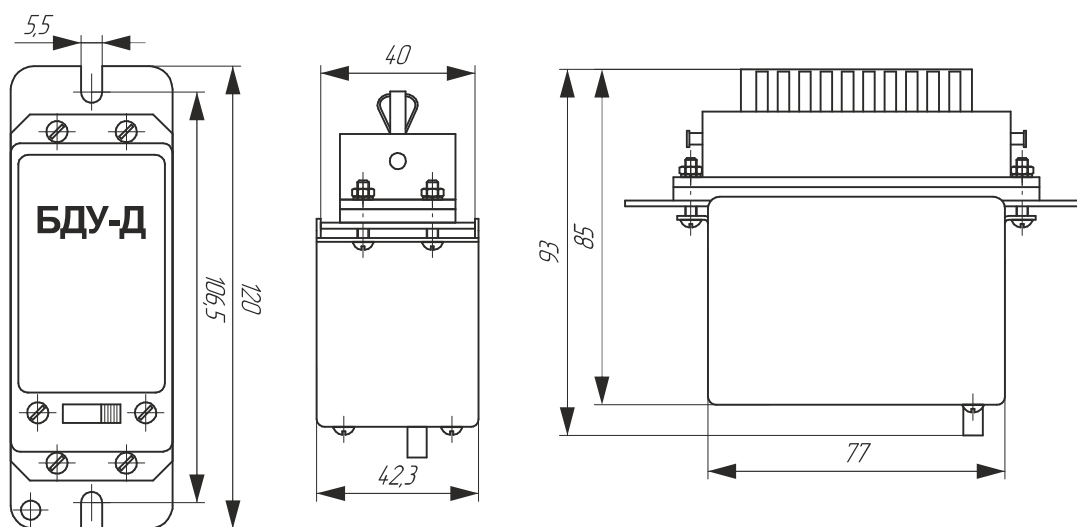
Габаритные и присоединительные размеры блока в исполнении БДУ-хД.1хх
